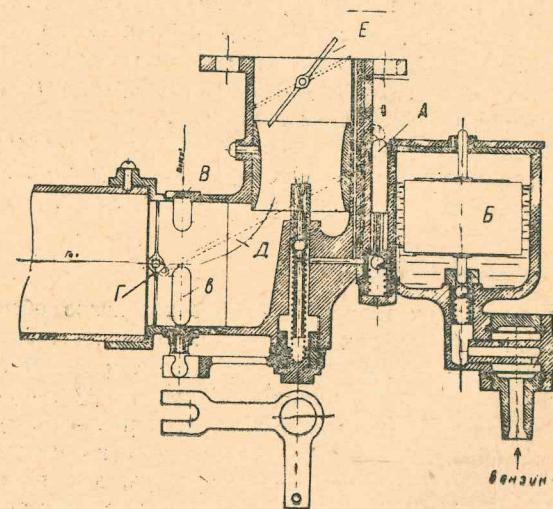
Смеситель установки „Барбье“. А — игла регулировки бензина, связанная с дросселем газа; Б — поплавковая камера; В — кольцо регулировки воздуха; В — отверстия для прохода воздуха; Г — дроссель газа; Д — связь дросселя газа с иглой регулировки бензина; Е — дроссель смеси
